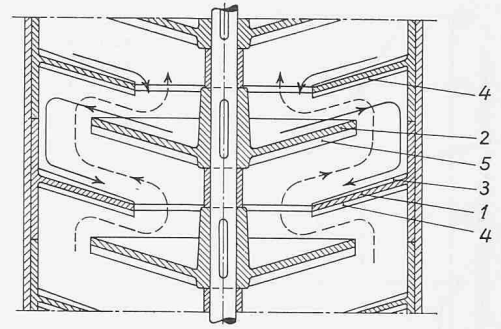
Einbauten einer Kolonne nach dem System Jost, Bezeichnungen im Text.
